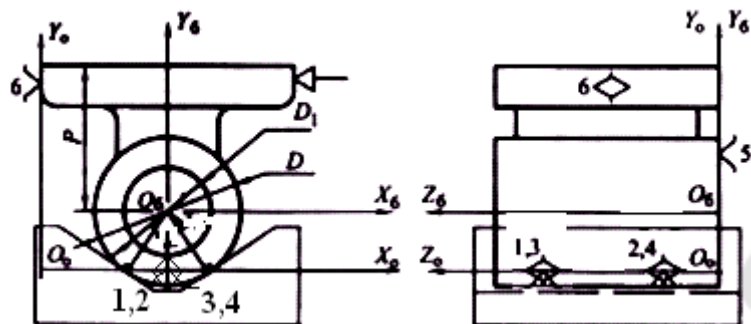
Несовпадение базовой и опорной систем координат - условие для возникновения погрешности схемы установки
